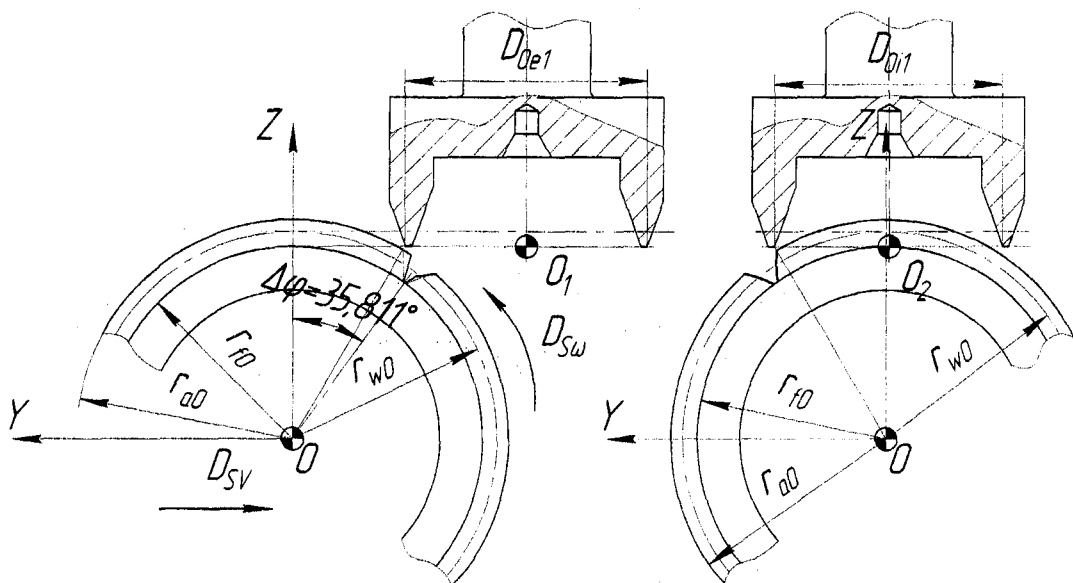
Движение обката при получистовой обработке впадины инструмента двусторонней зуборезной резцовой головкой
